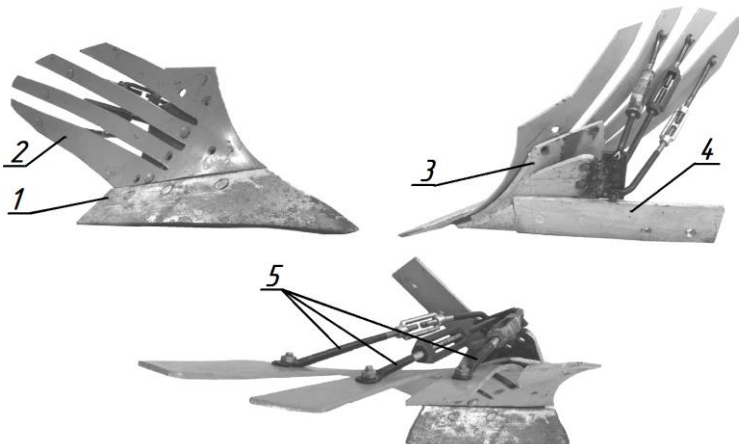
Экспериментальный корпус плуга с пластинчатым отвалом:
